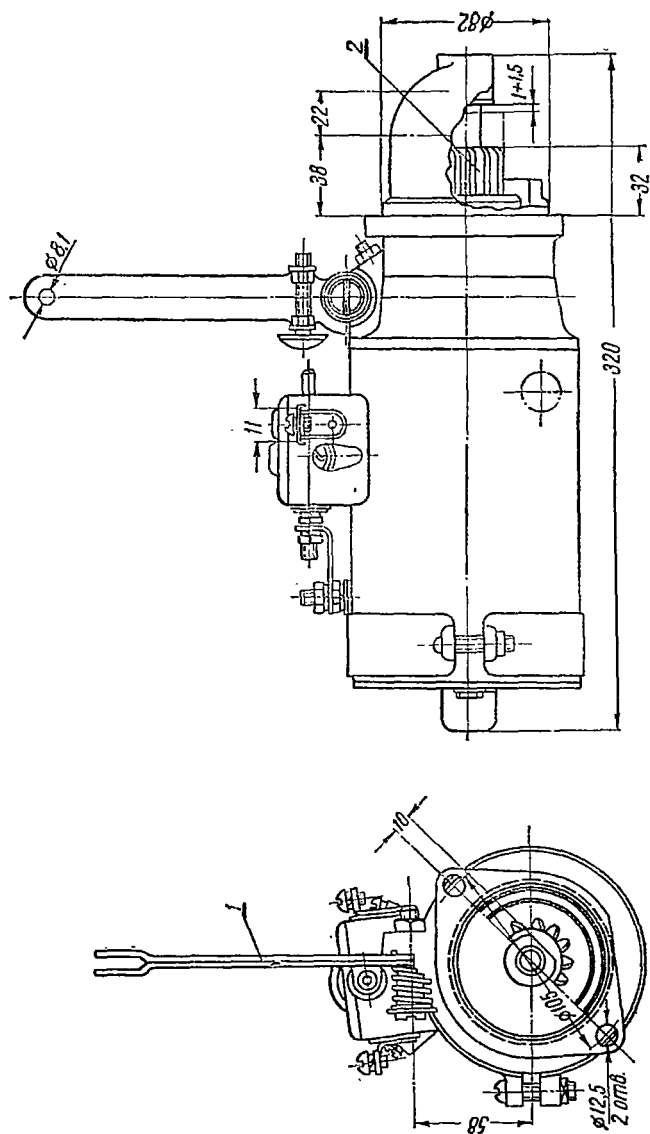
Габаритные размеры стартера СТ15-Б:
